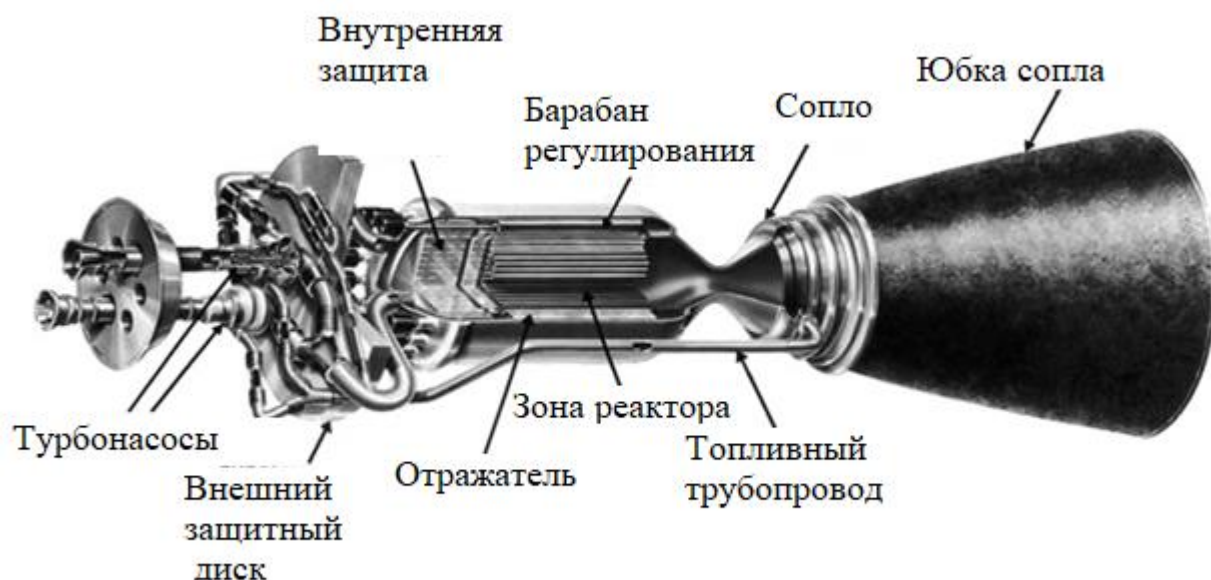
Общий вид ядерного ракетного двигателя [14]
